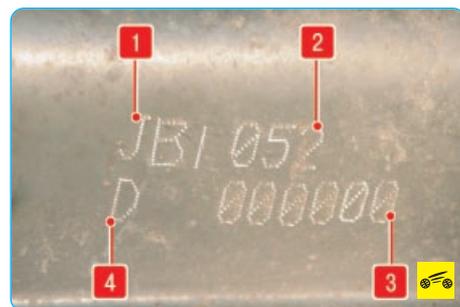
Идентификационные данные коробки передач: 1 – тип коробки передач; 2 – модификация коробки передач; 3 – порядковый номер коробки передач; 4 – код завода-изготовителя
